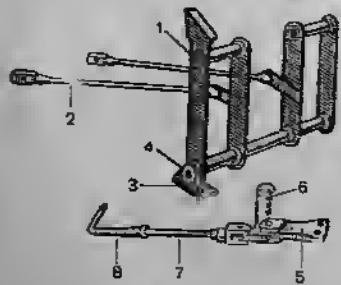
Педаль ножного тормоза и стопорный механизм:
